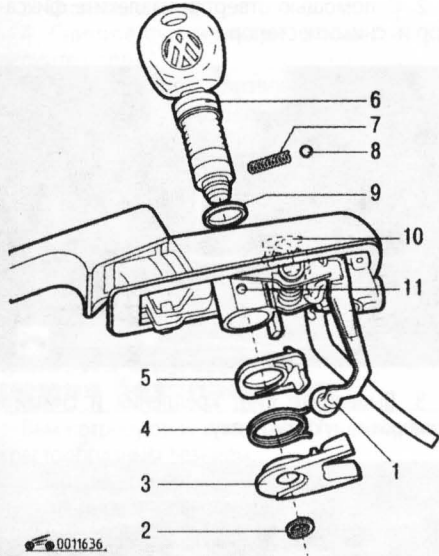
Детали цилиндра замка: 1 – регулировочный болт; 2 – пружинное стопорное кольцо; 3 – рычаг; 4, 7 – пружины; 5 – ограничитель; 6 – цилиндр замка; 8 – шарик; 9 – уплотнительное кольцо; 10 – микропереключатель; 11 – монтажное отверстие
